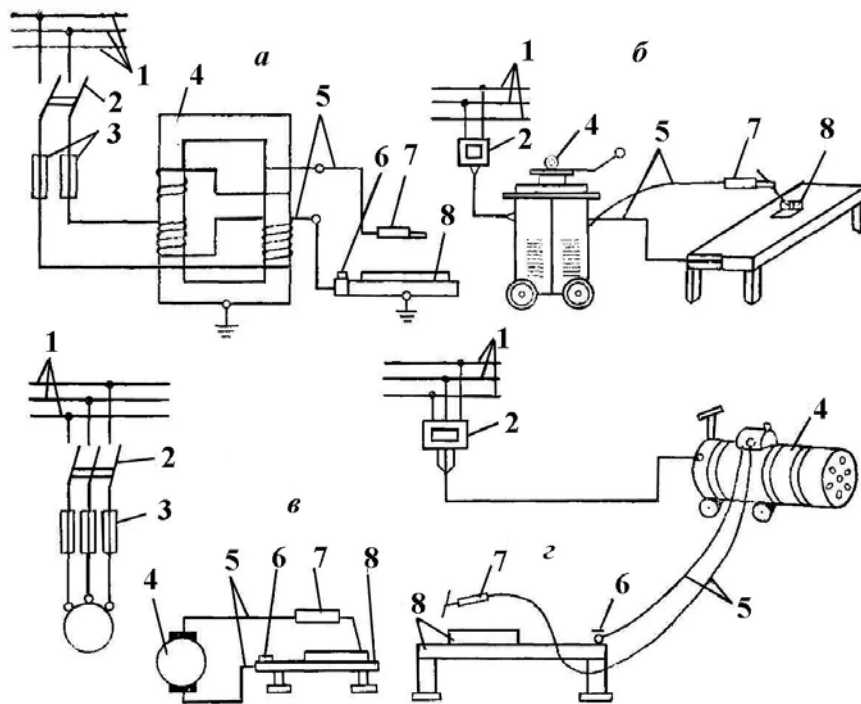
Пристрій для ручного електродугового зварювання:
